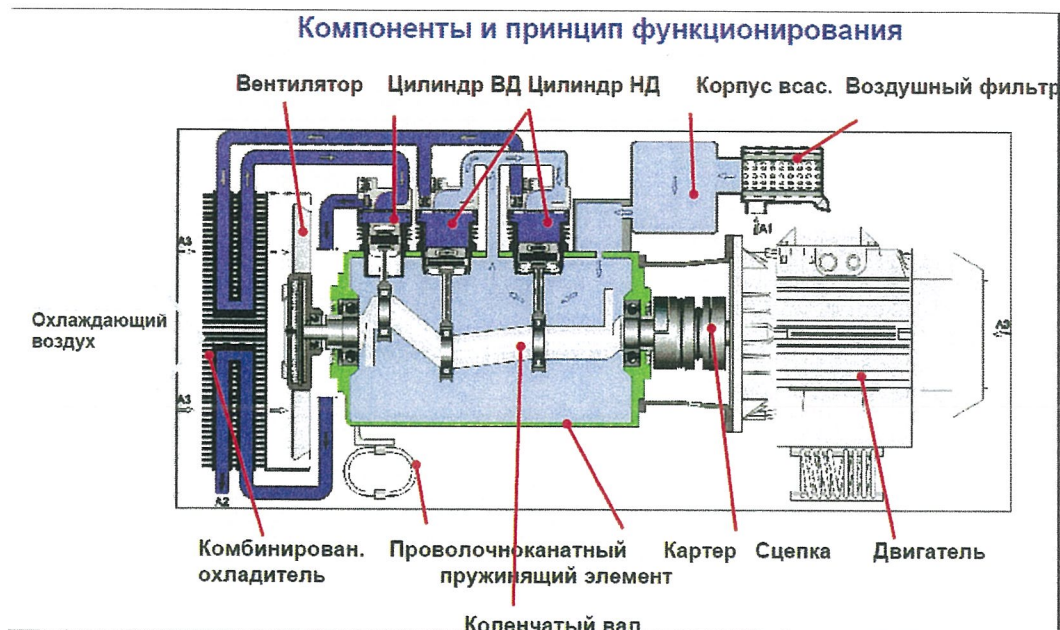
Безмасляный компрессорный агрегат типа «W-180Т»
